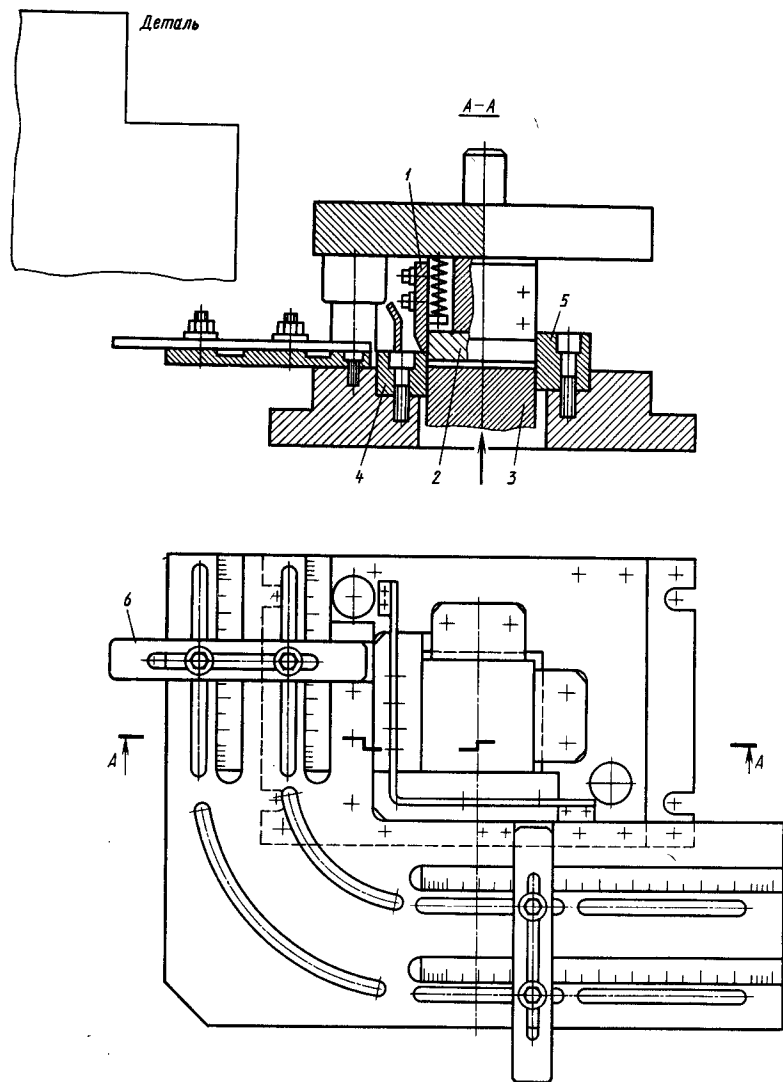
Универсально-переналаживаемый штамп для обрезки угла в заготовке
